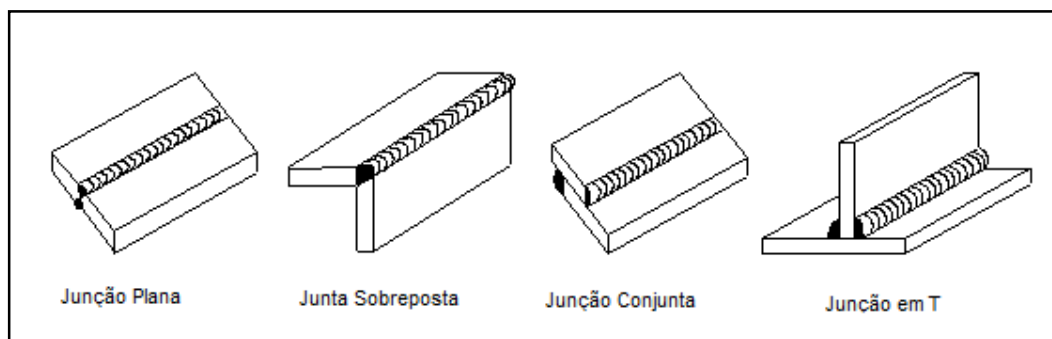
Tipos de junta na soldagem com eletrodo revestido
